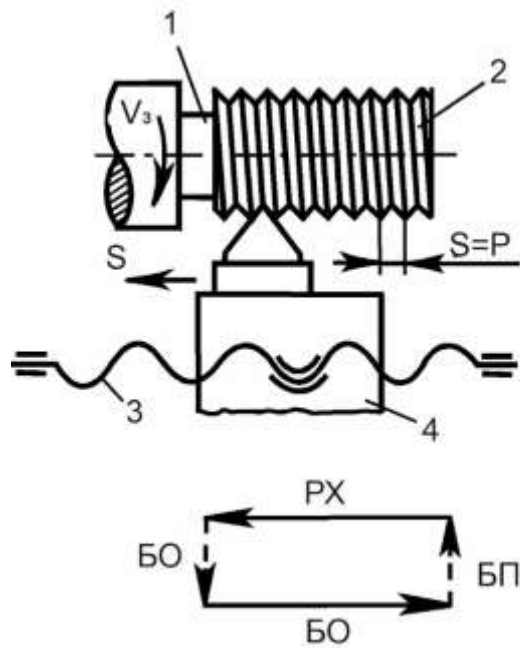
Схема обробки та циклограма роботи при нарізанні зовнішньої різьби: 1 – заготовка; 2 – різьбова поверхня; 3 – ходовий гвинт; 4 – супорт із встановленим різцем.
